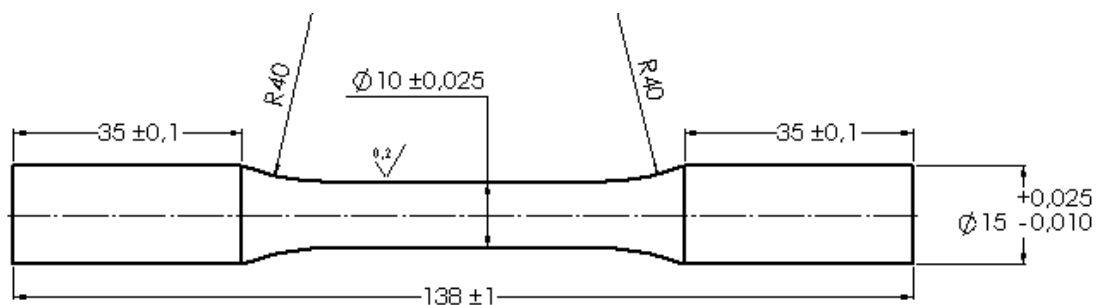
Geometria do corpo de prova de fadiga (dimensões em mm).
